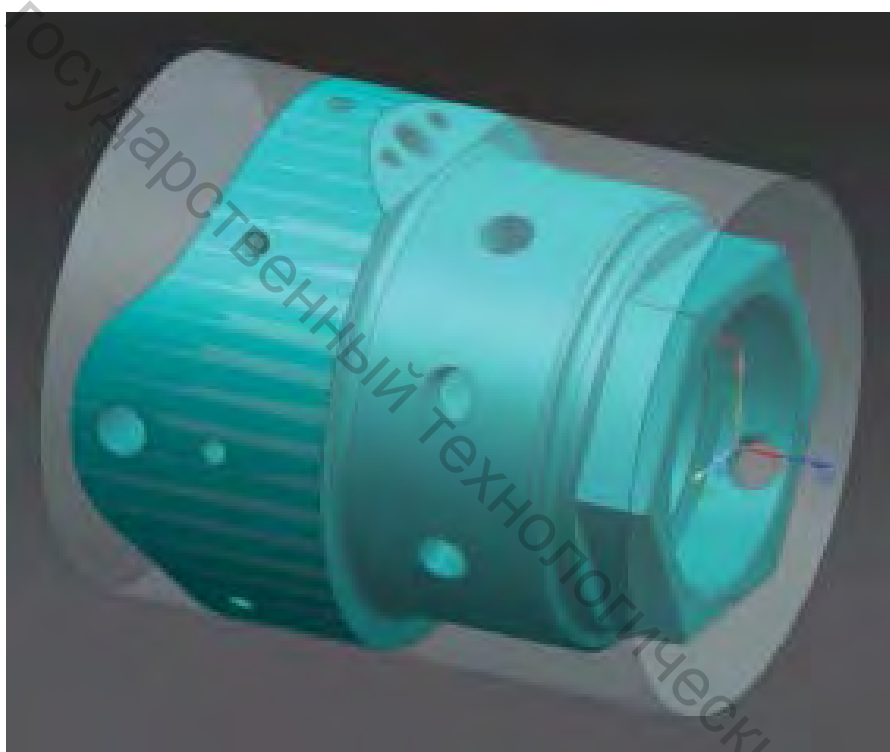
Привязка СКС и РСК к детали при токарно-фрезерной обработке
